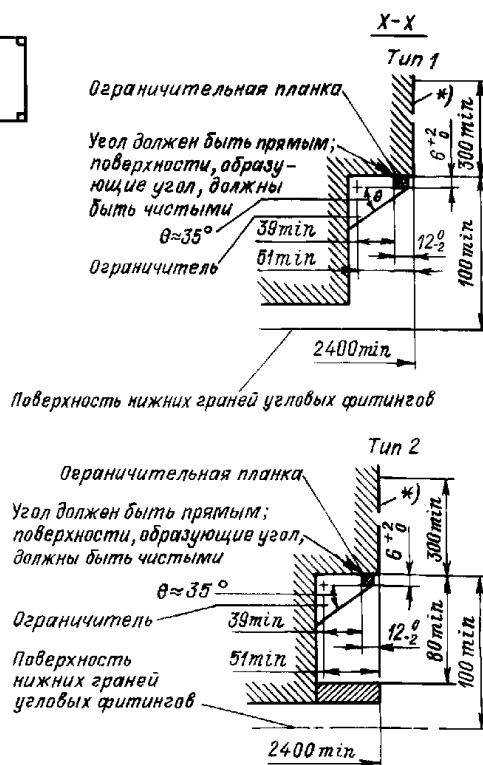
Расположение зон подъема, размеры, мм, и конструкция площадок для клещевых захватов
